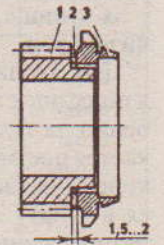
Шестерня с установленной шайбой: 1 - шестерня; 2 - шайба; 3 - зубчатый венец
